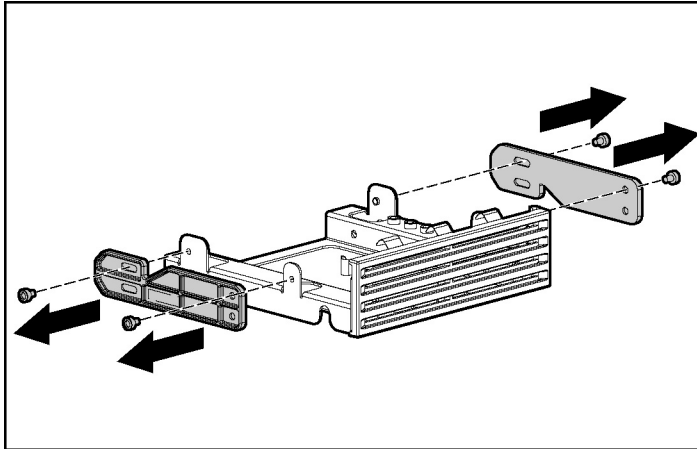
Entfernen der Schienen vom Blindmodul des Schachts für Wechselmedienlaufwerke
